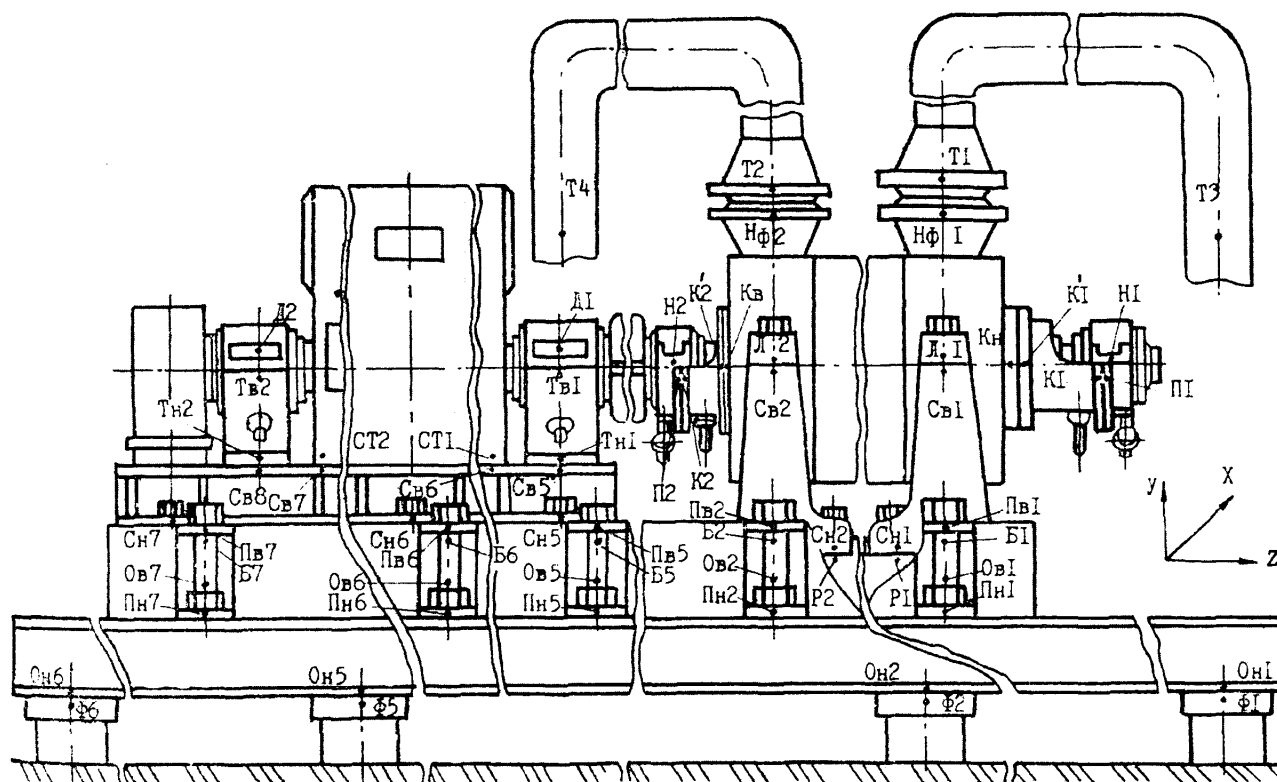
Схема розміщення контрольних точок на корпусі ЦНС-180-1900
